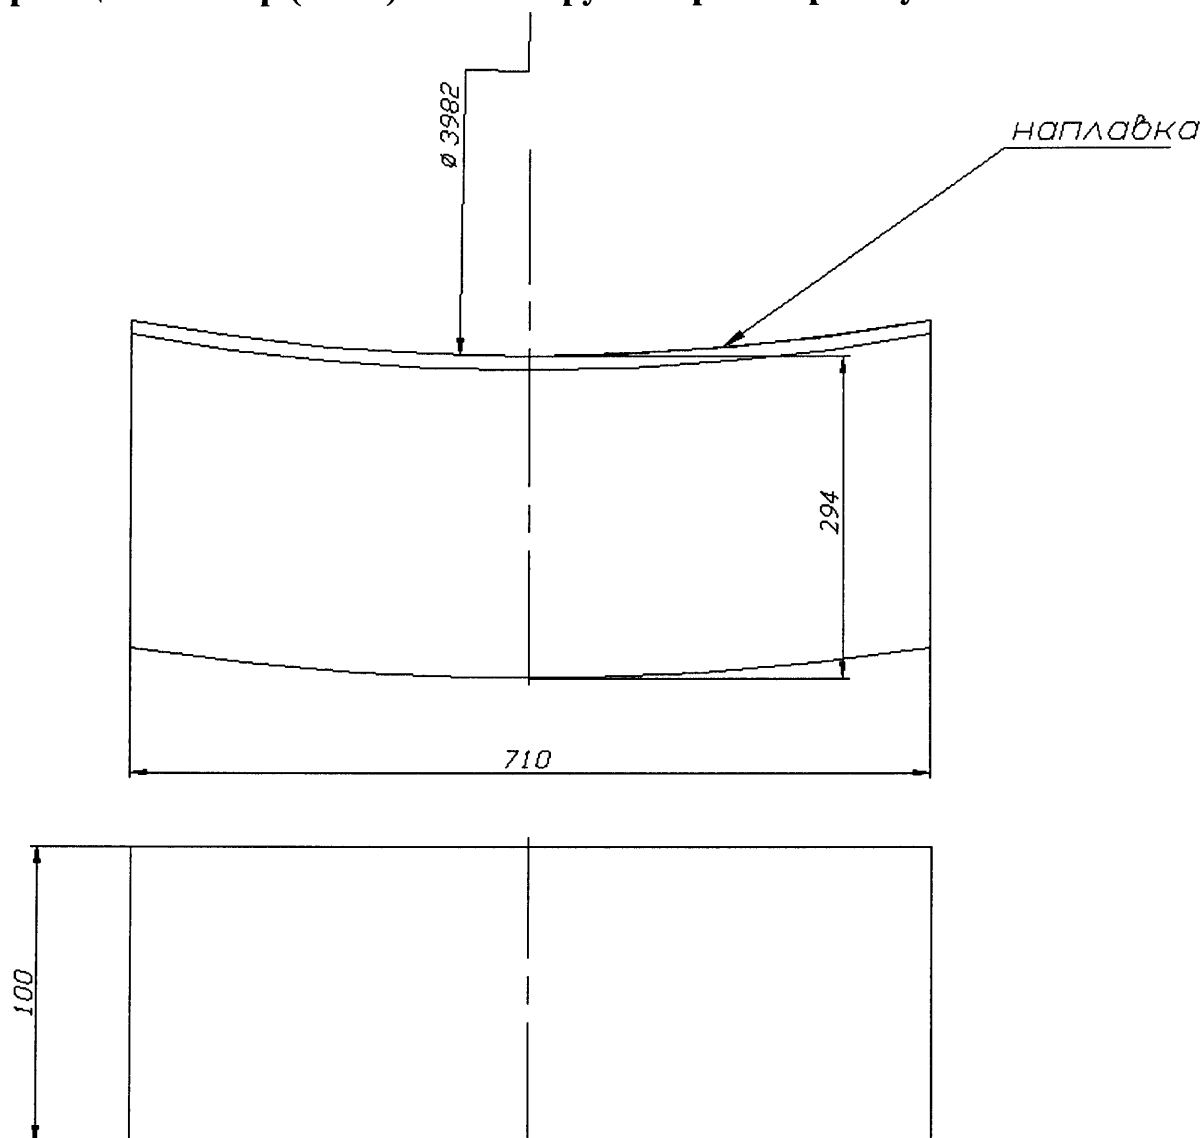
Образец-имитатор (СОП) зоны патрубков
